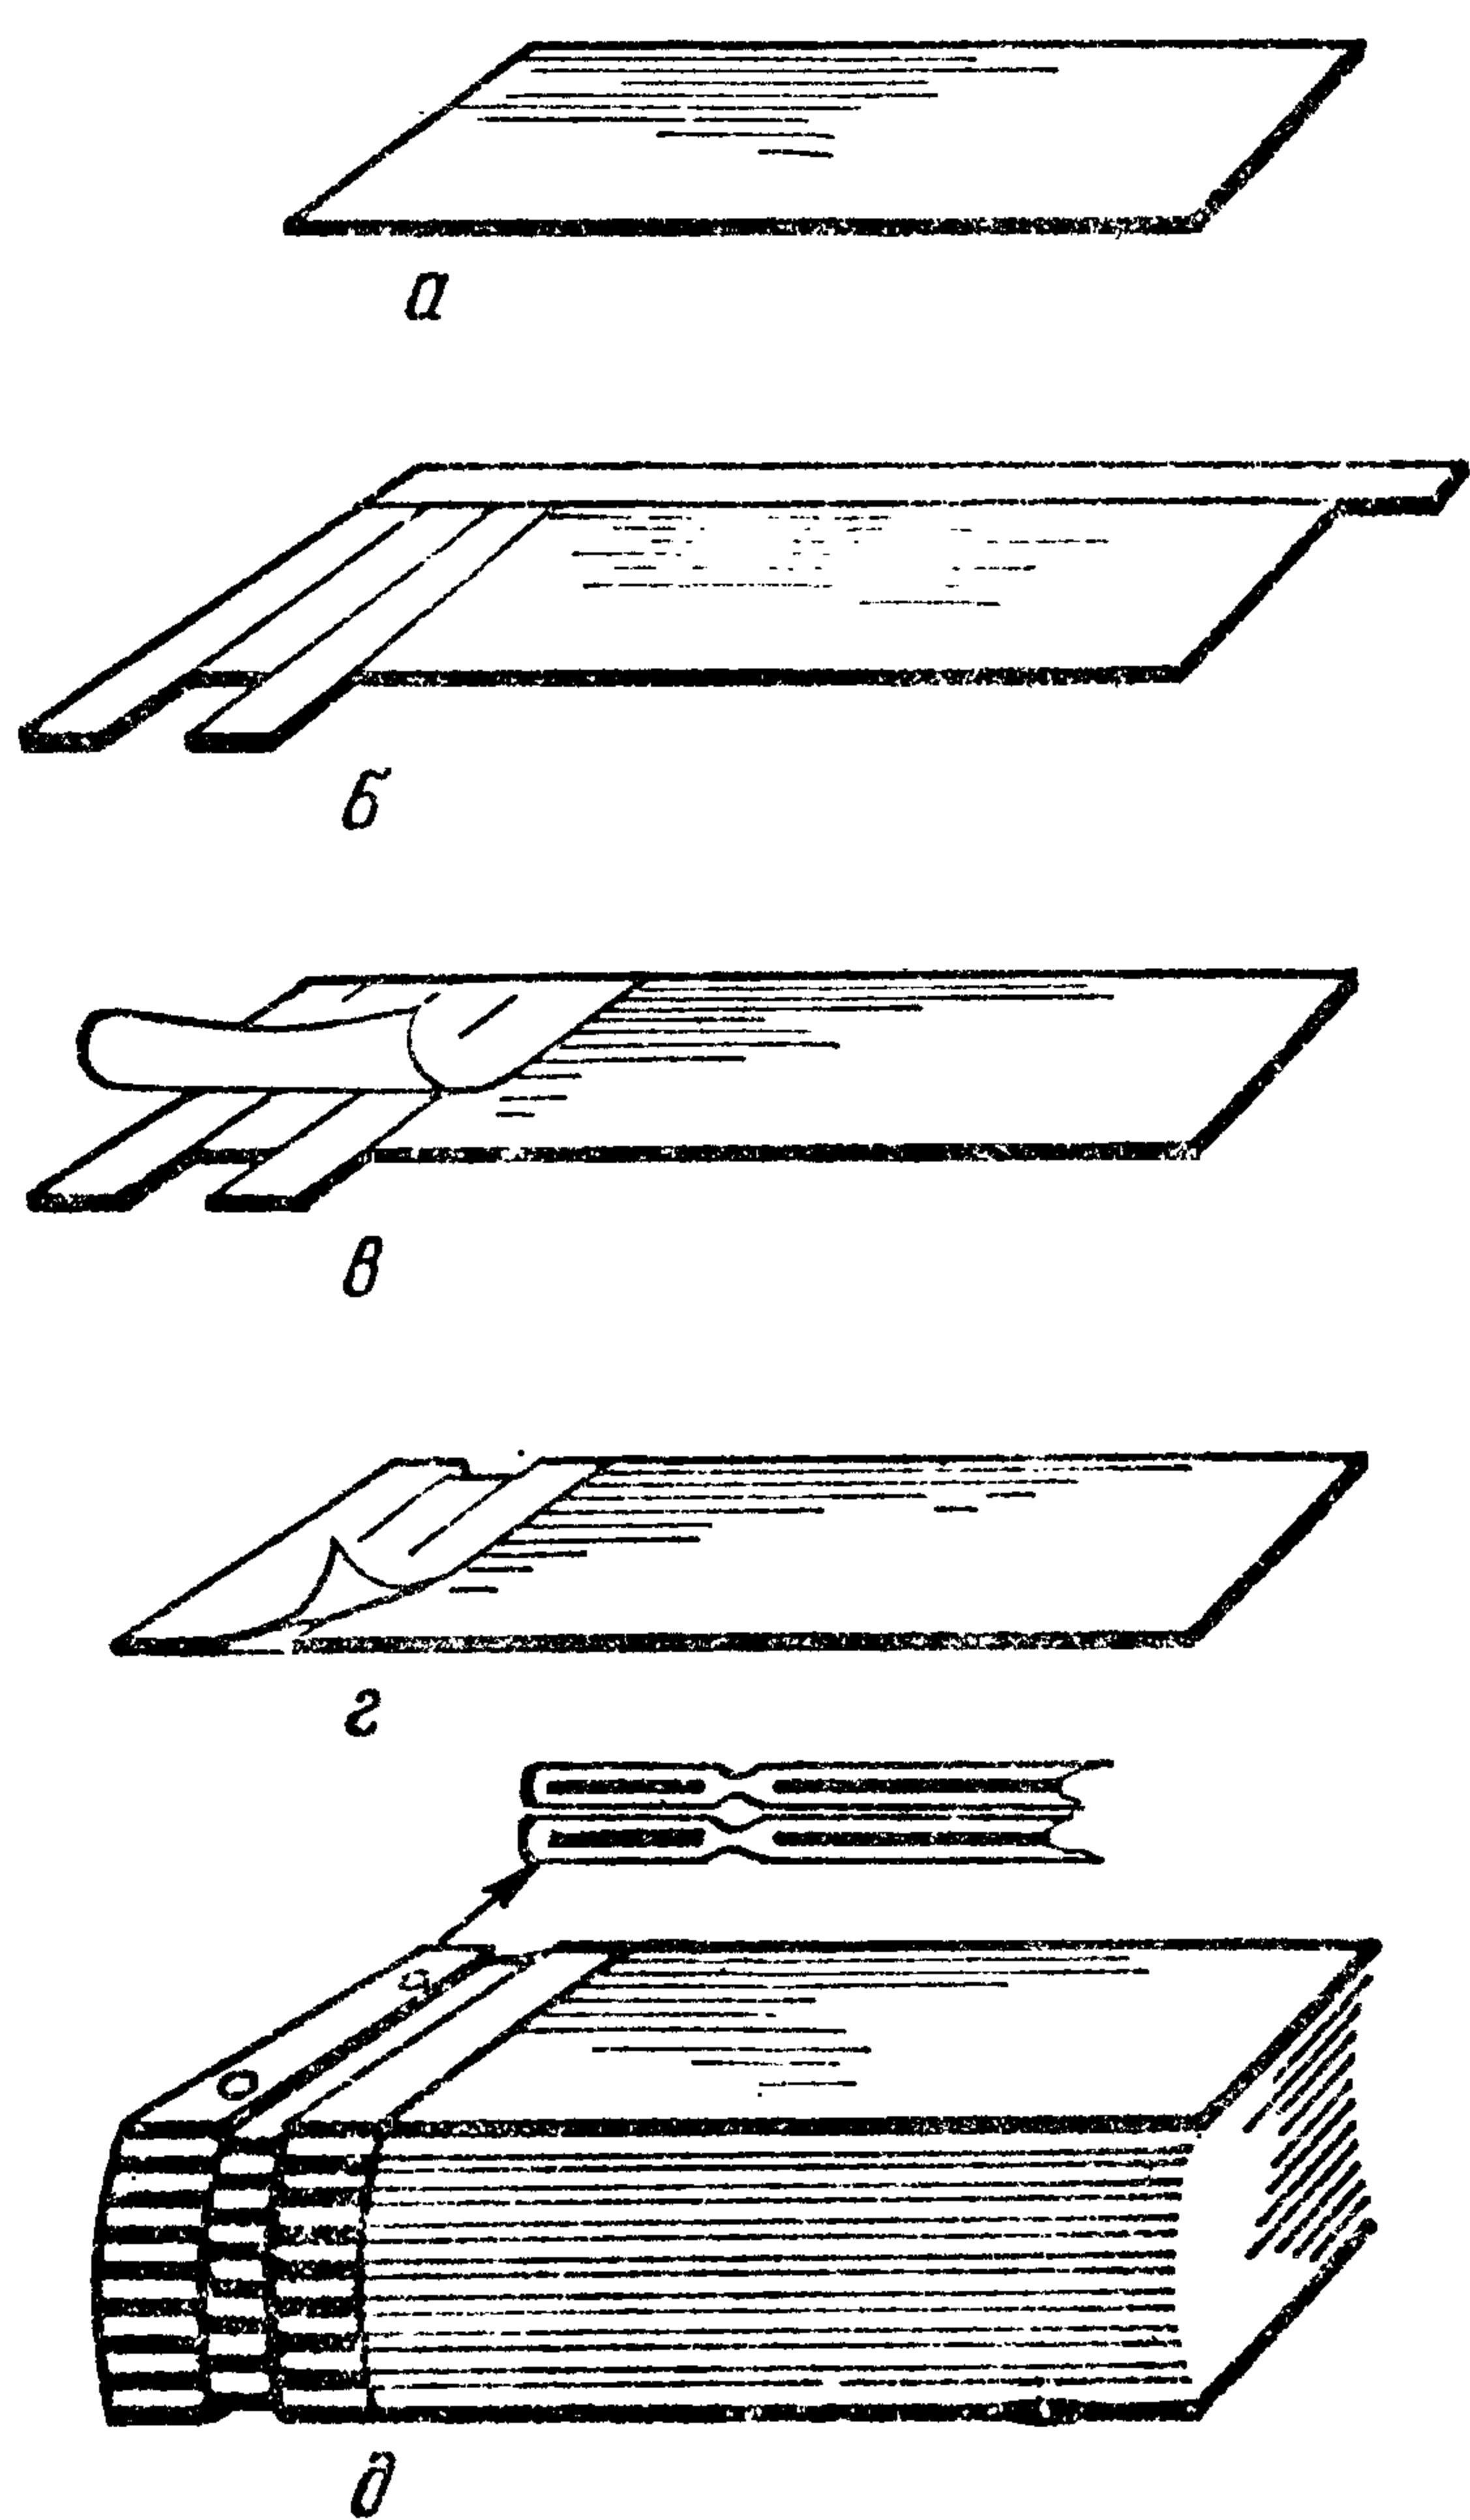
Изготовление альбомных листов с шарниром: а — картонная заготовка; б — расположение деталей на шаблоне; в — наклейка ткани на кромку листа и шарнир; г — оклейка тканью тыльной стороны шарнира; д — блок в сборе.
